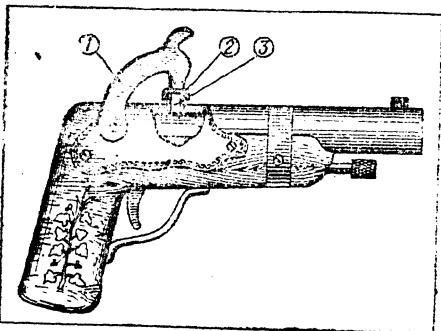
Пистолет кремневого зажигания. Спусковой механизм: 1—курок; 2—барашек; 3—верхний зажим кремня; 4—огниво; 5—кремнь; 6— пороховой лоток; 7—затравочное отверстие; 8—предохранительная скоба; 9—спусковой крючок
